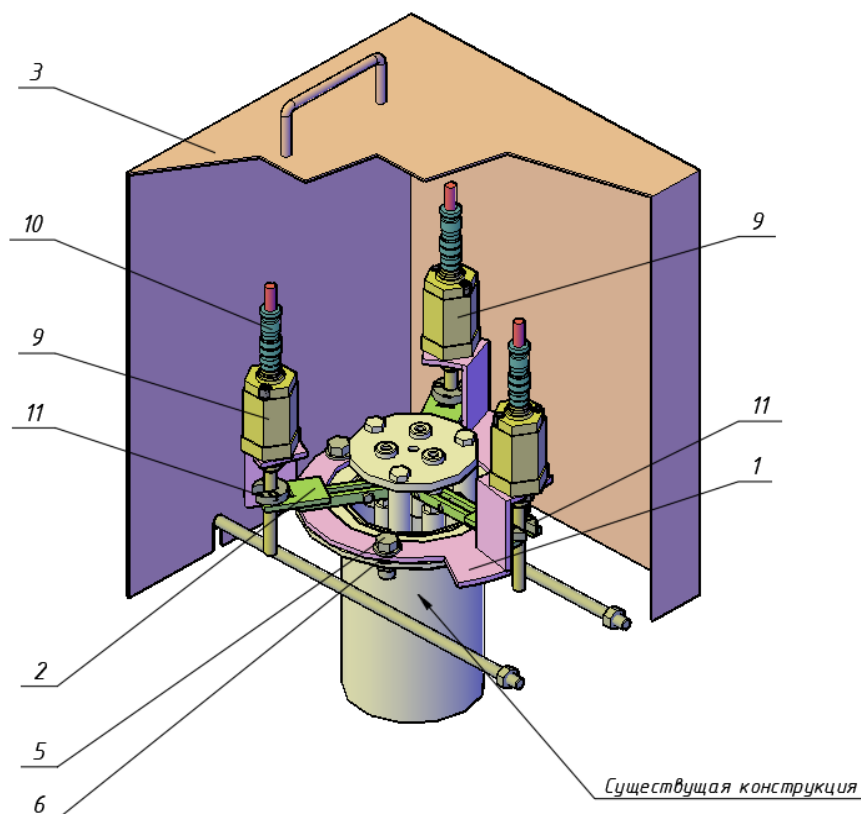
Конструкция крепления датчиков VTL7 на трехбазном деформометре: 1 – конструкция 1; 2 – конструкция 2, 3 – защитный кожух; 4 – опорный стержень; 5 – болт M12×45; 6 – шайба 12; 7 – гайка M12; 8 – гайка M10; 9 – Датчик Balluff VTL-E10-M0025-V-S32; 10 – Разъем Balluff VKS-S 32M-C; 11 – магнит VTL5 VTL5-P-1013-4S
